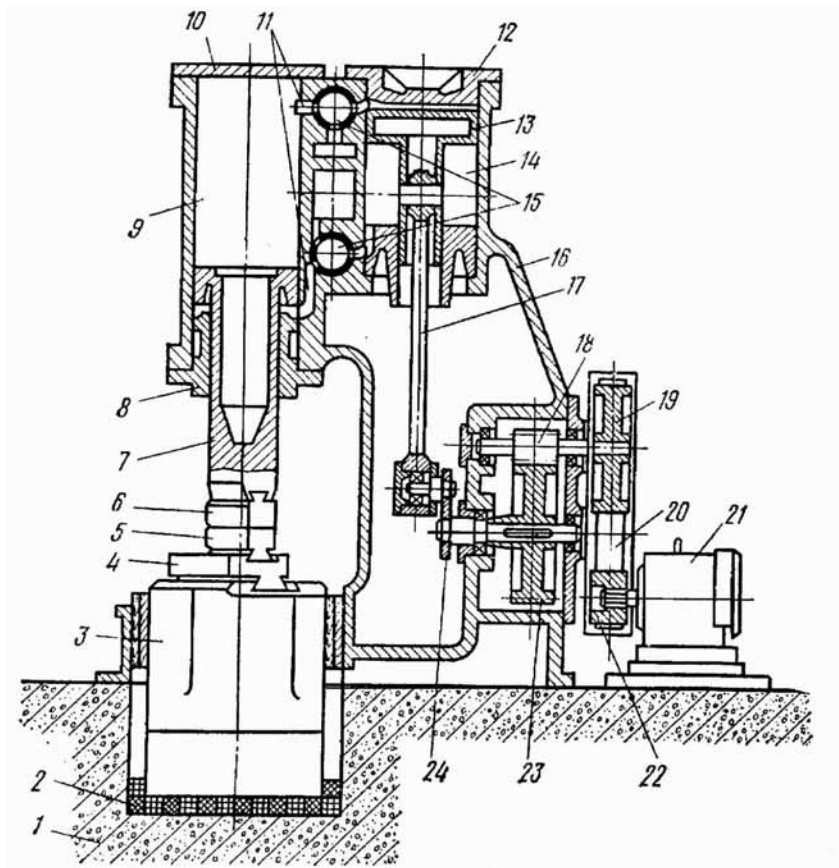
Схема пневматического двухцилиндрового одностоечного ковочного молота: 1 – фундамент; 2 – деревянные брусья; 3 – шабот; 4 – промежуточная подушка; 5 – нижний боек; 6 – верхний боек; 7 – баба; 8 – нижняя крышка рабочего цилиндра; 9 – рабочий цилиндр; 10 – верхняя крышка рабочего цилиндра; 11 – каналы; 12 – верхняя крышка компрессорного цилиндра; 13 – поршень компрессорного цилиндра; 14 – компрессорный цилиндр; 15 – распределительные краны; 16 – станина; 17 – шатун; 18 и 23 – зубчатые колеса; 19 – маховик; 20 – ремень плоский; 21 – электродвигатель; 22 – шкив; 24 – кривошип
